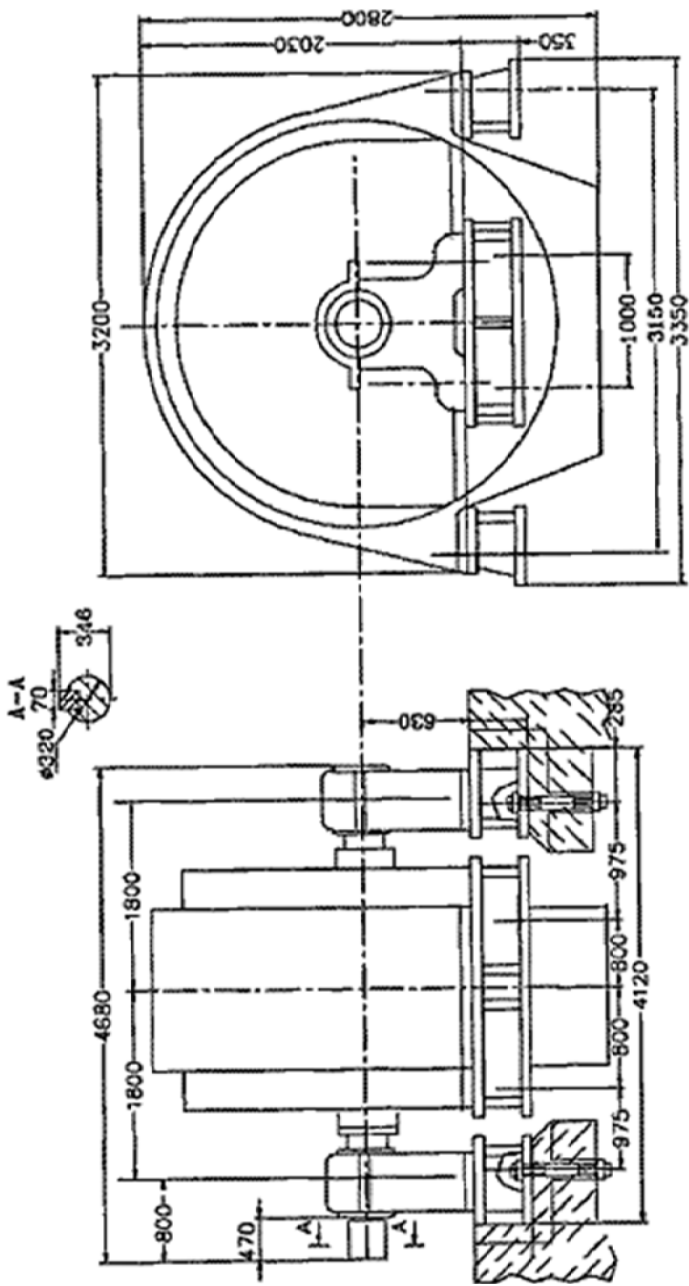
Габаритные, установочные и присоединительные размеры синхронной машины серии СДНЗ-2-19-104-10 УХЛ14
